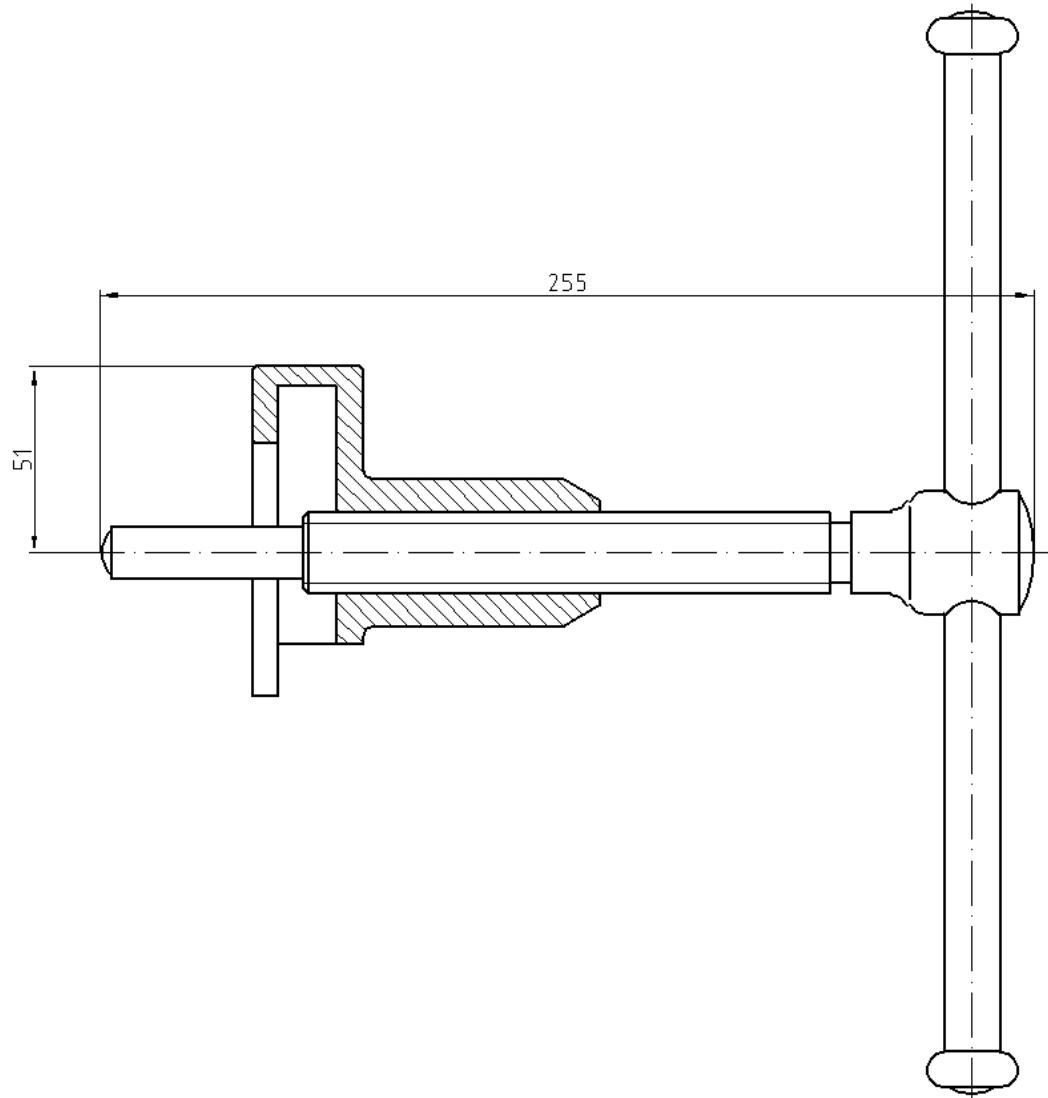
ЗМ 7814-5111, Съемник для снятия ступицы шкива коленчатого вала
